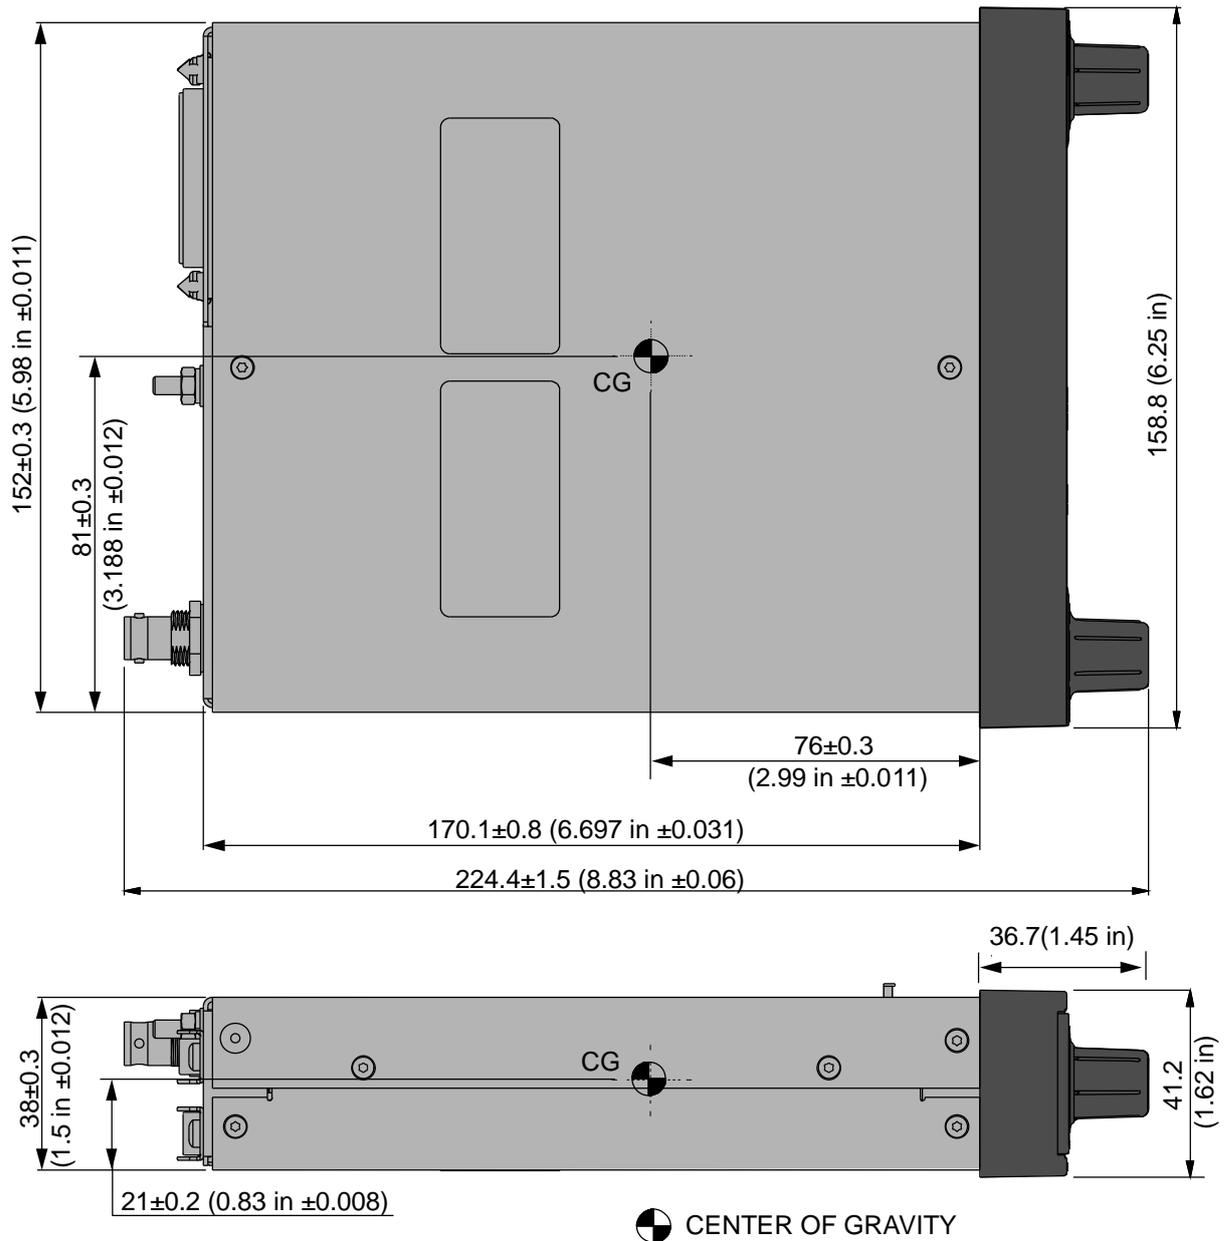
Abmessungen AR6203 (Draufsicht, Seitenansicht)
